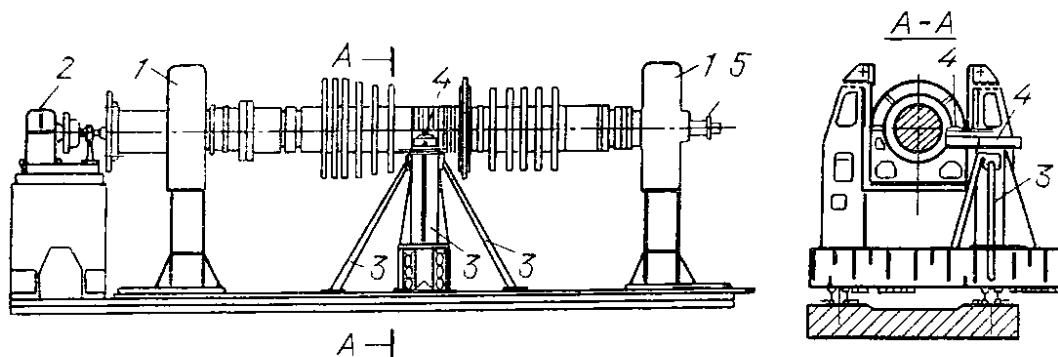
Устройство для восстановления ресурса роторов: 1 — опоры ротора; 2 — тихоходный (4 об/мин) привод для механической обработки ротора; 3 — стойка для установки суппорта и шлифовального устройства; 4 — суппорт; 5 — фиксатор осевого положения ротора
